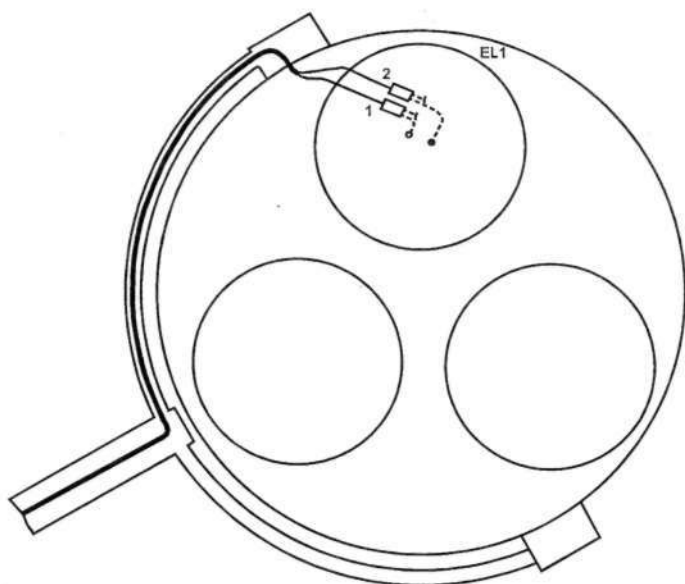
Подсоединение жгута электропроводки в блоке освещения 60 светильника СР-5-«Е-ЭМА»
